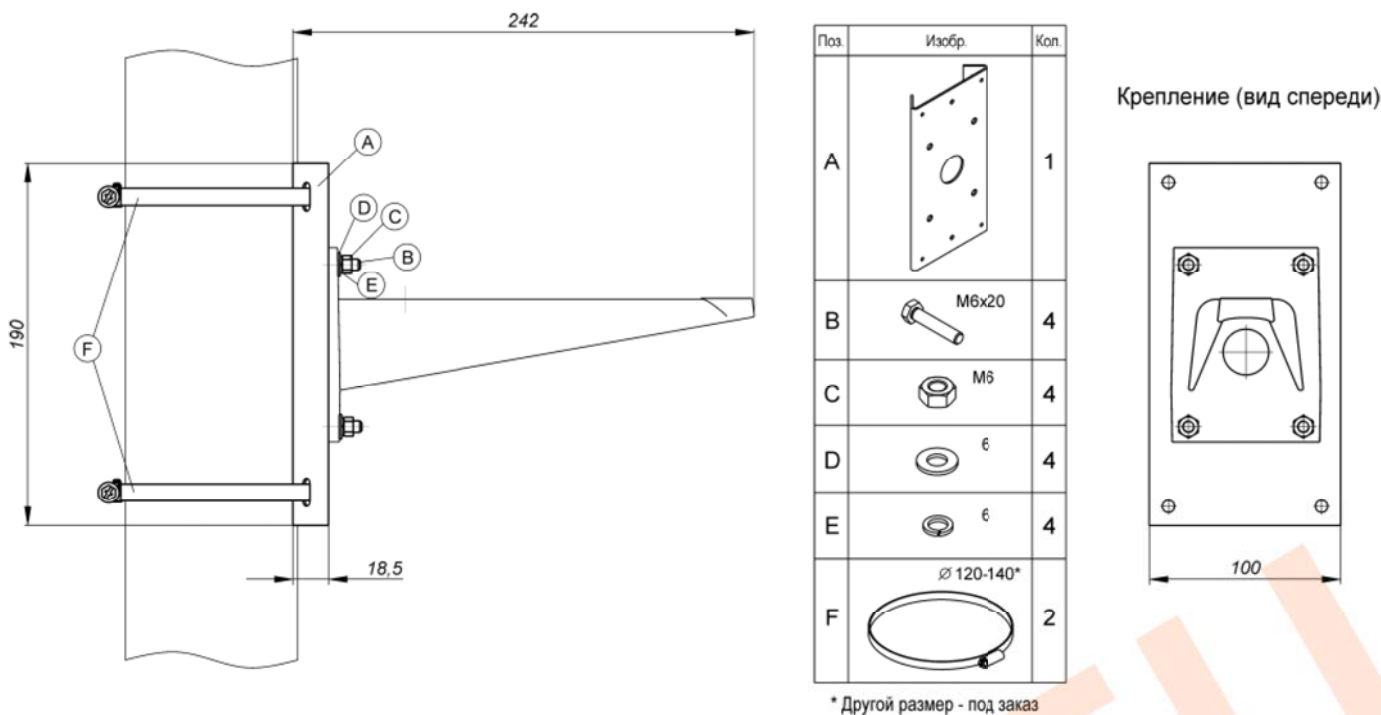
Монтаж кронштейна КС-1 на опору (круглую или квадратную)
